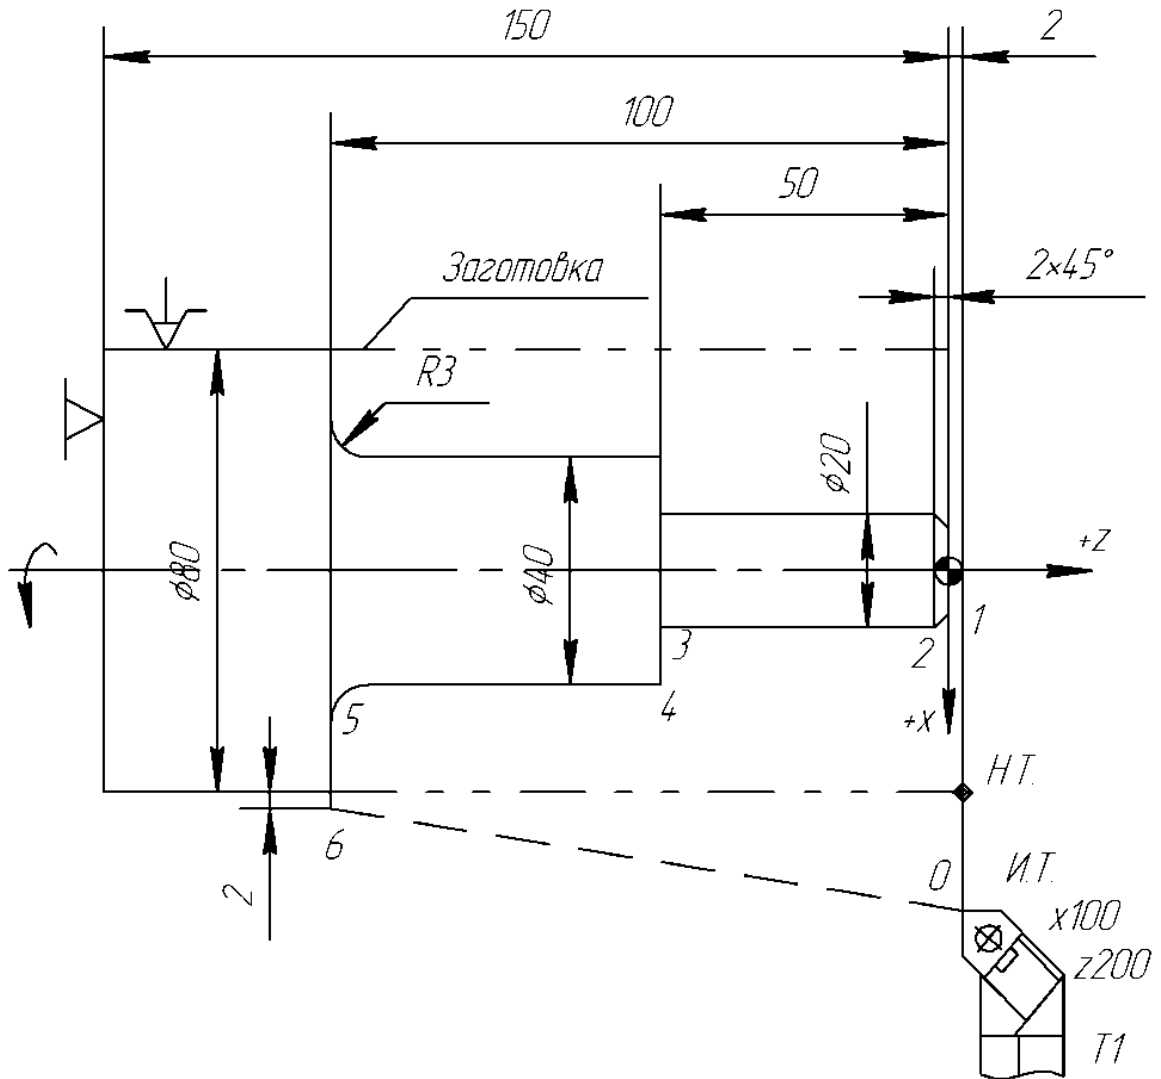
Схема до програмування обробки ступеневого валика з циліндричної заготовки по циклу L08
